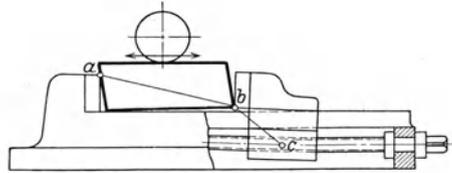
Schraubstock minderwertiger Konstruktion.
